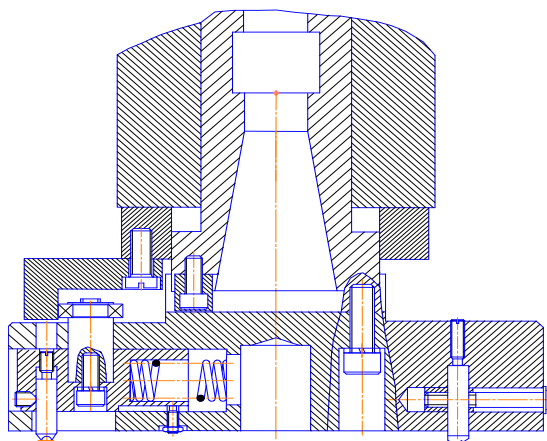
Конструкція торцевої фрези для реалізації запропонованої схеми обробки
